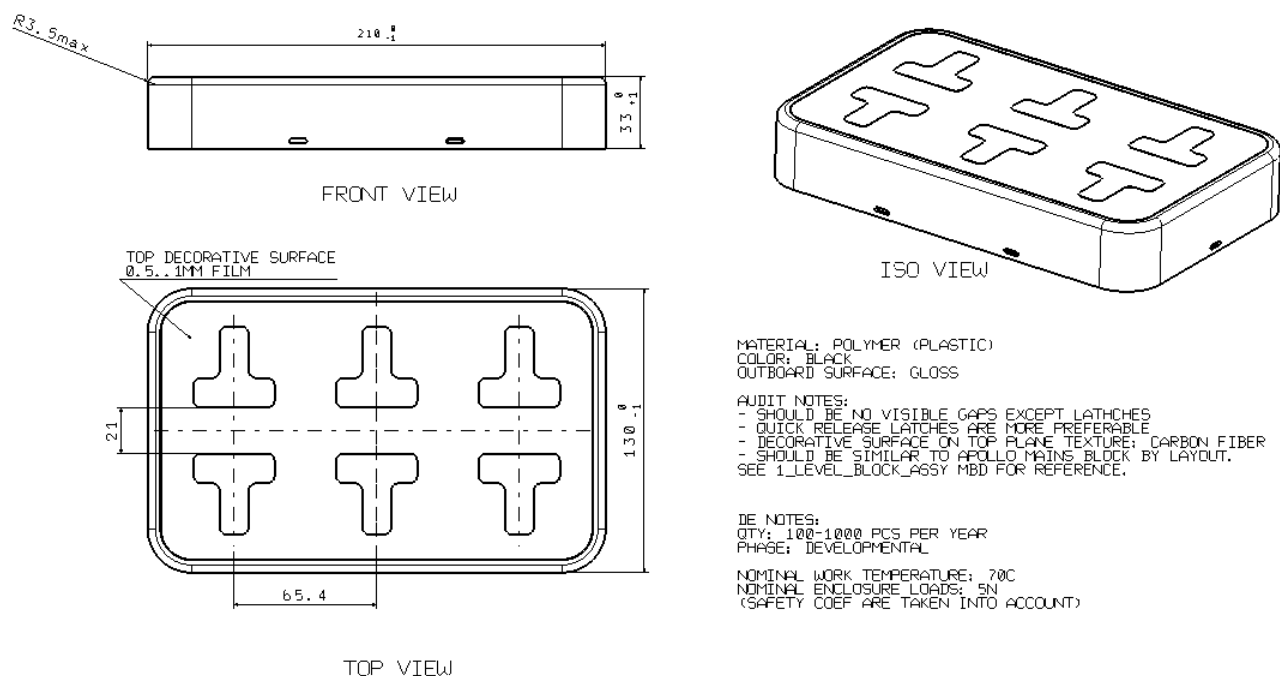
Попереднє визначення конструкції корпусу
